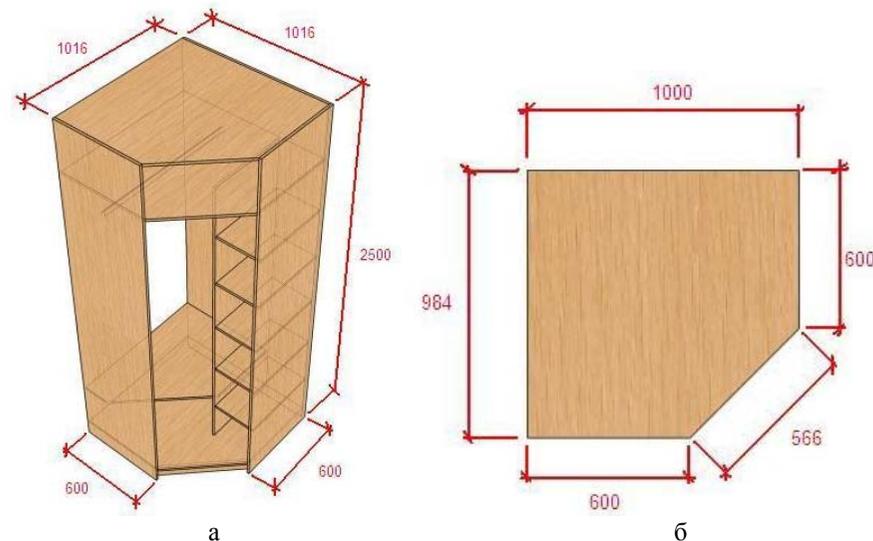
Тумба углового шкафа: а – общий вид; б – вид сверху
